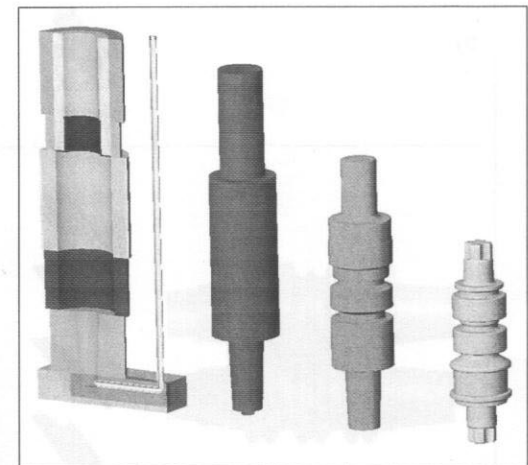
Herstellungstufen einer Walze, v. l. n. r. Walzenform, Gußkörper, vorkalibrierte Walze und fertigbearbeitete Profilwalze
